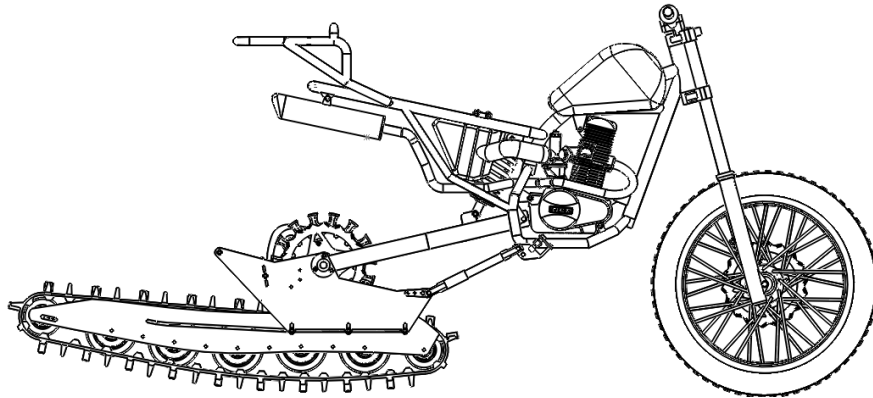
Ensamblaje final del prototipo Moto-Oruga
